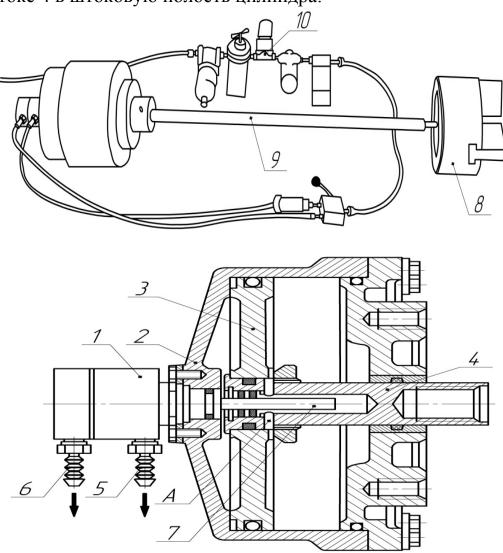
Пневматический вращающийся цилиндр: 1 - муфта; 2 - цилиндр; 3 - поршень; 4 - шток; 5, 6 - ниппели; 7 - стержень; 8 - патрон; 9 - тяга; 10 - пневмоаппаратура
